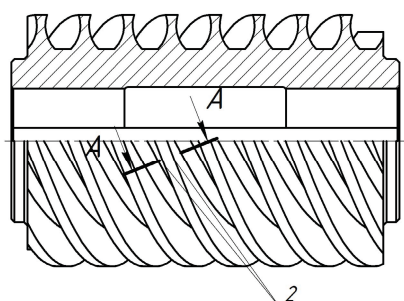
Усовершенствованная конструкция шевера с винтовыми режущими кромками
